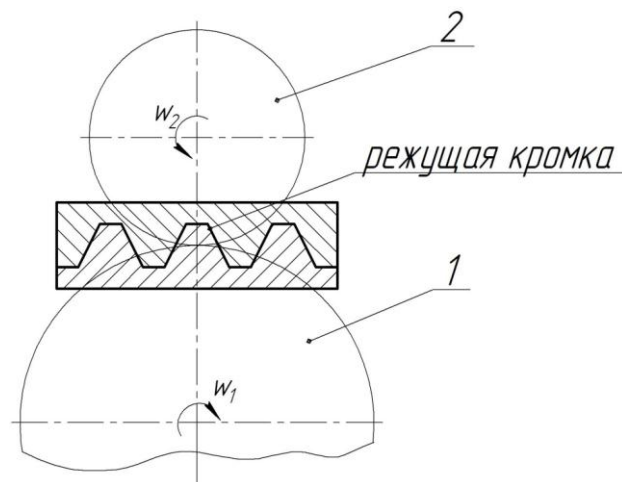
Формообразование зубчатых колес при помощи инструментальной рейки
